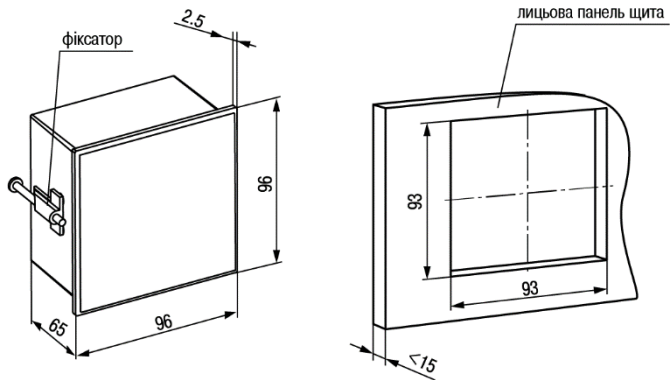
Габаритні розміри корпусу Щ1
